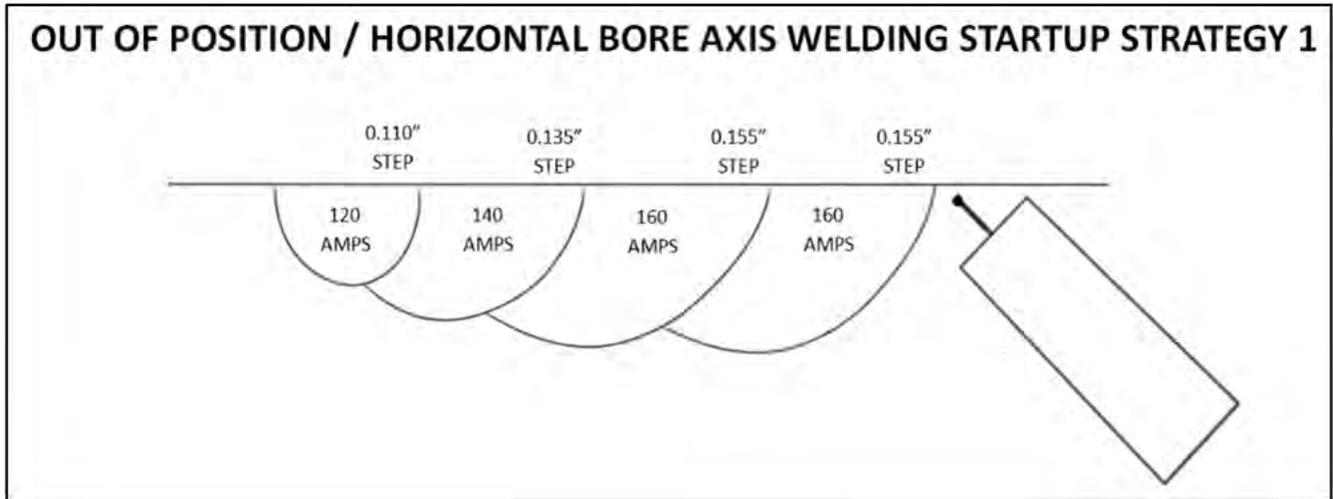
STRATÉGIE 1 POUR LE DÉMARRAGE DU SOUDAGE HORS POSITION/AXE D'ALÉSAGE HORIZONTAL
